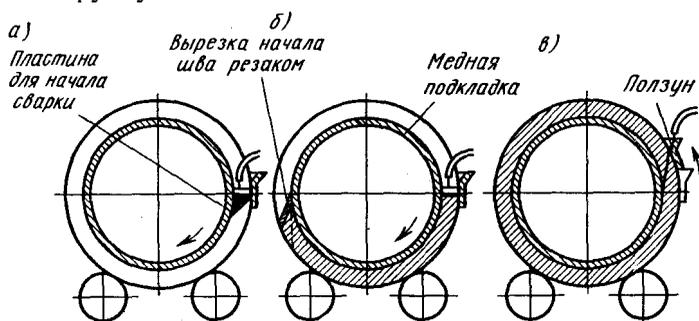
Схема электрошлаковой сварки кольцевых швов
